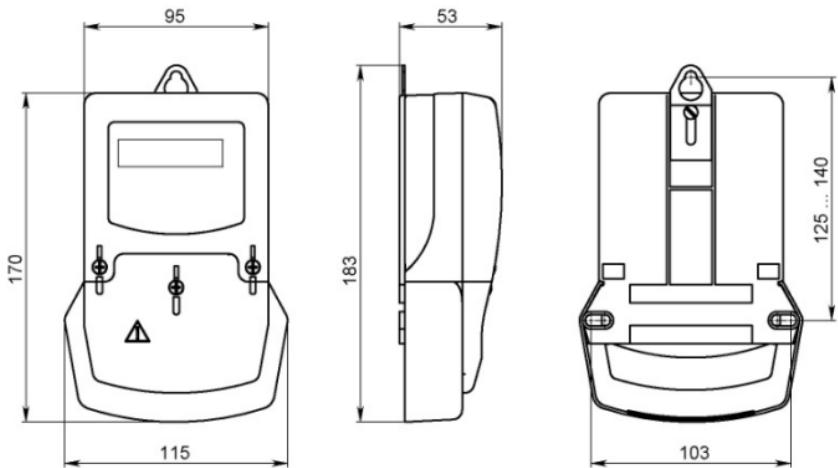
Габаритные и установочные размеры счетчика в корпусе S6
